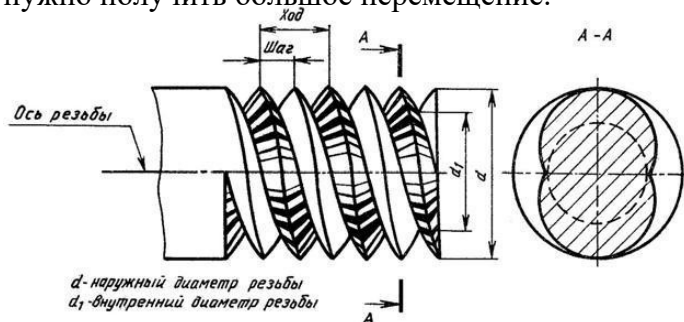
Резьба цилиндрическая двухзаходная
